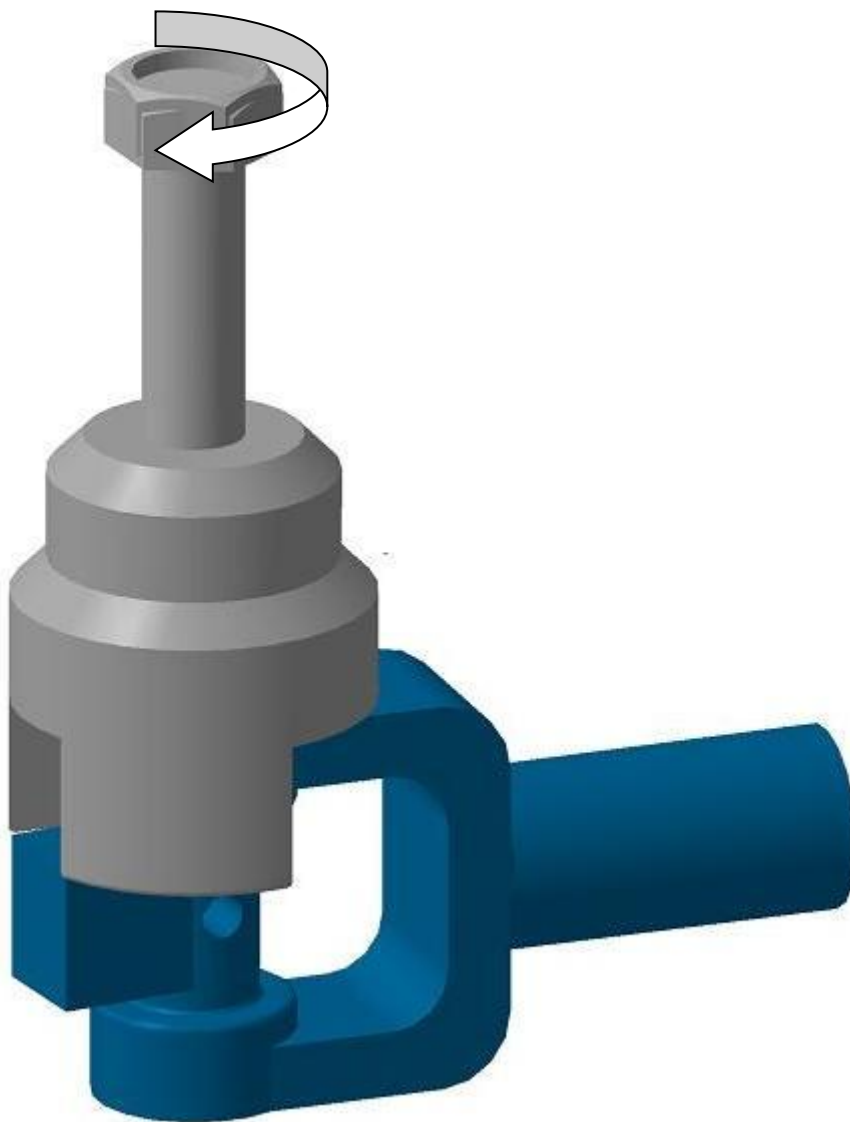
Приспособление для сборки разборки шарниров карданного вала рулевого управления
